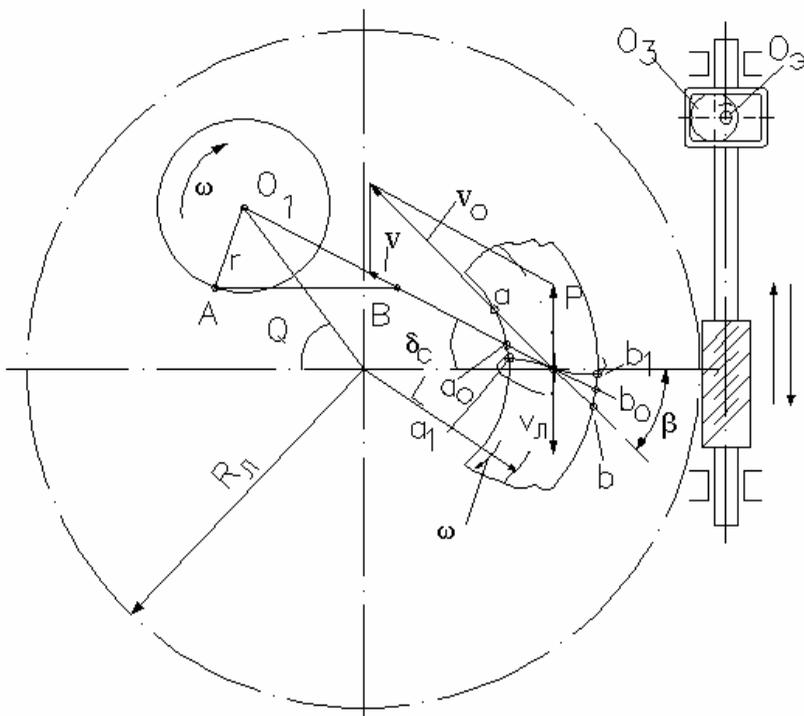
Схема обработки конического зубчатого колеса на станке 5284
